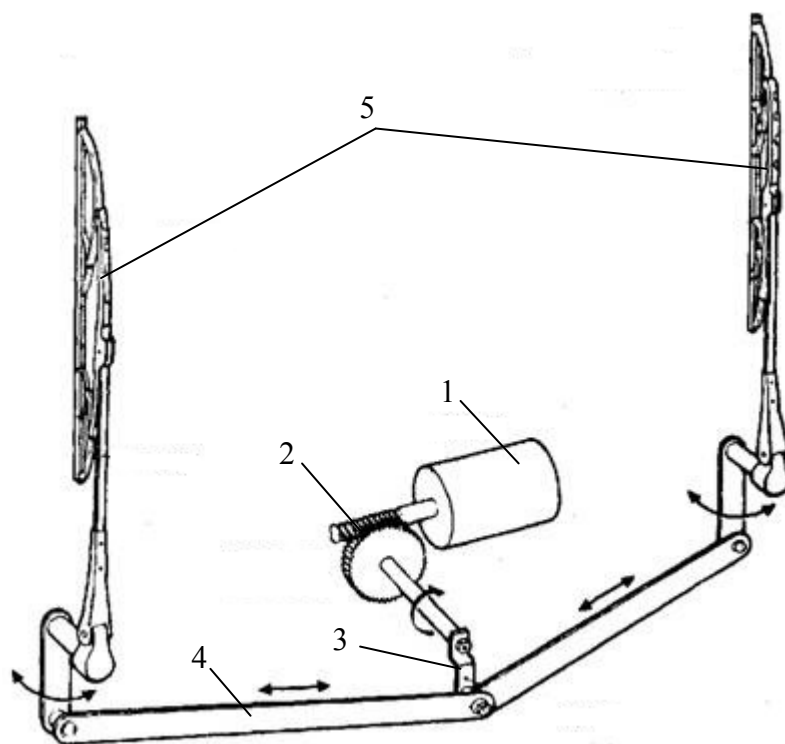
Klikový mechanismus, provedení s pákovým převodem
